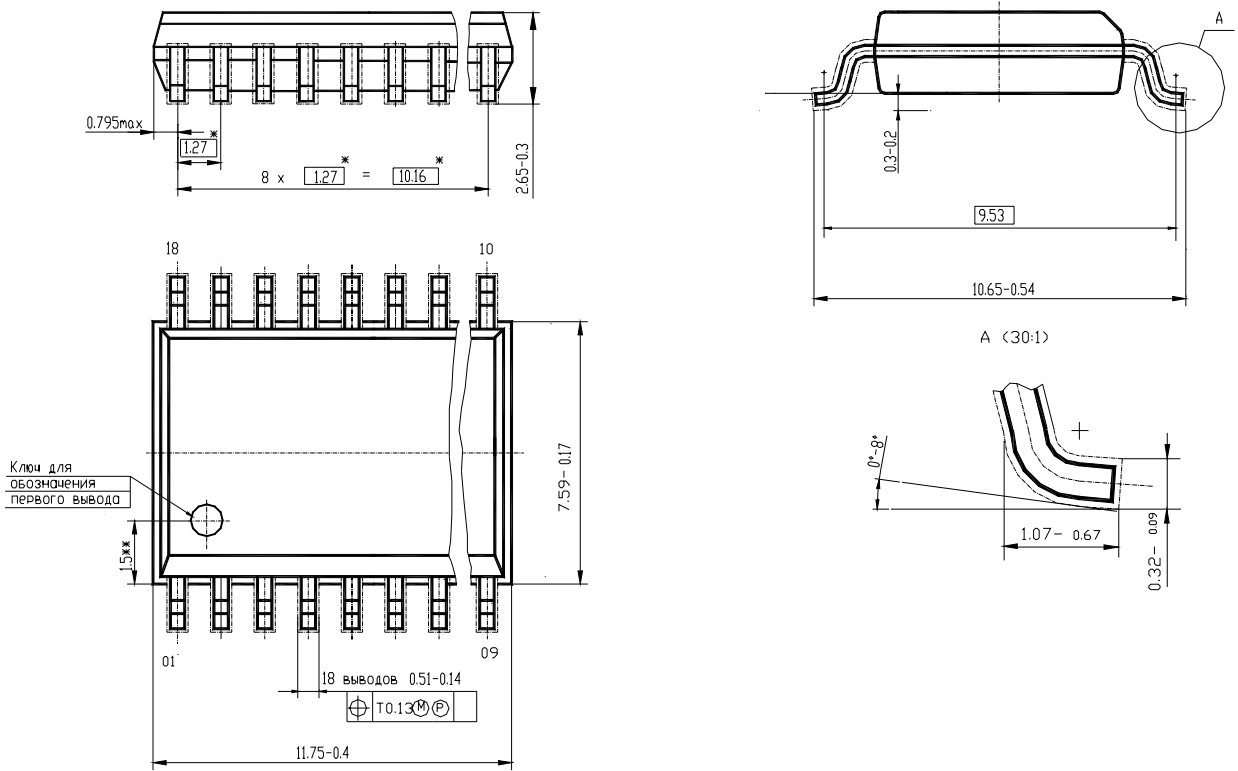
Габаритный чертеж корпуса MS-013AB
